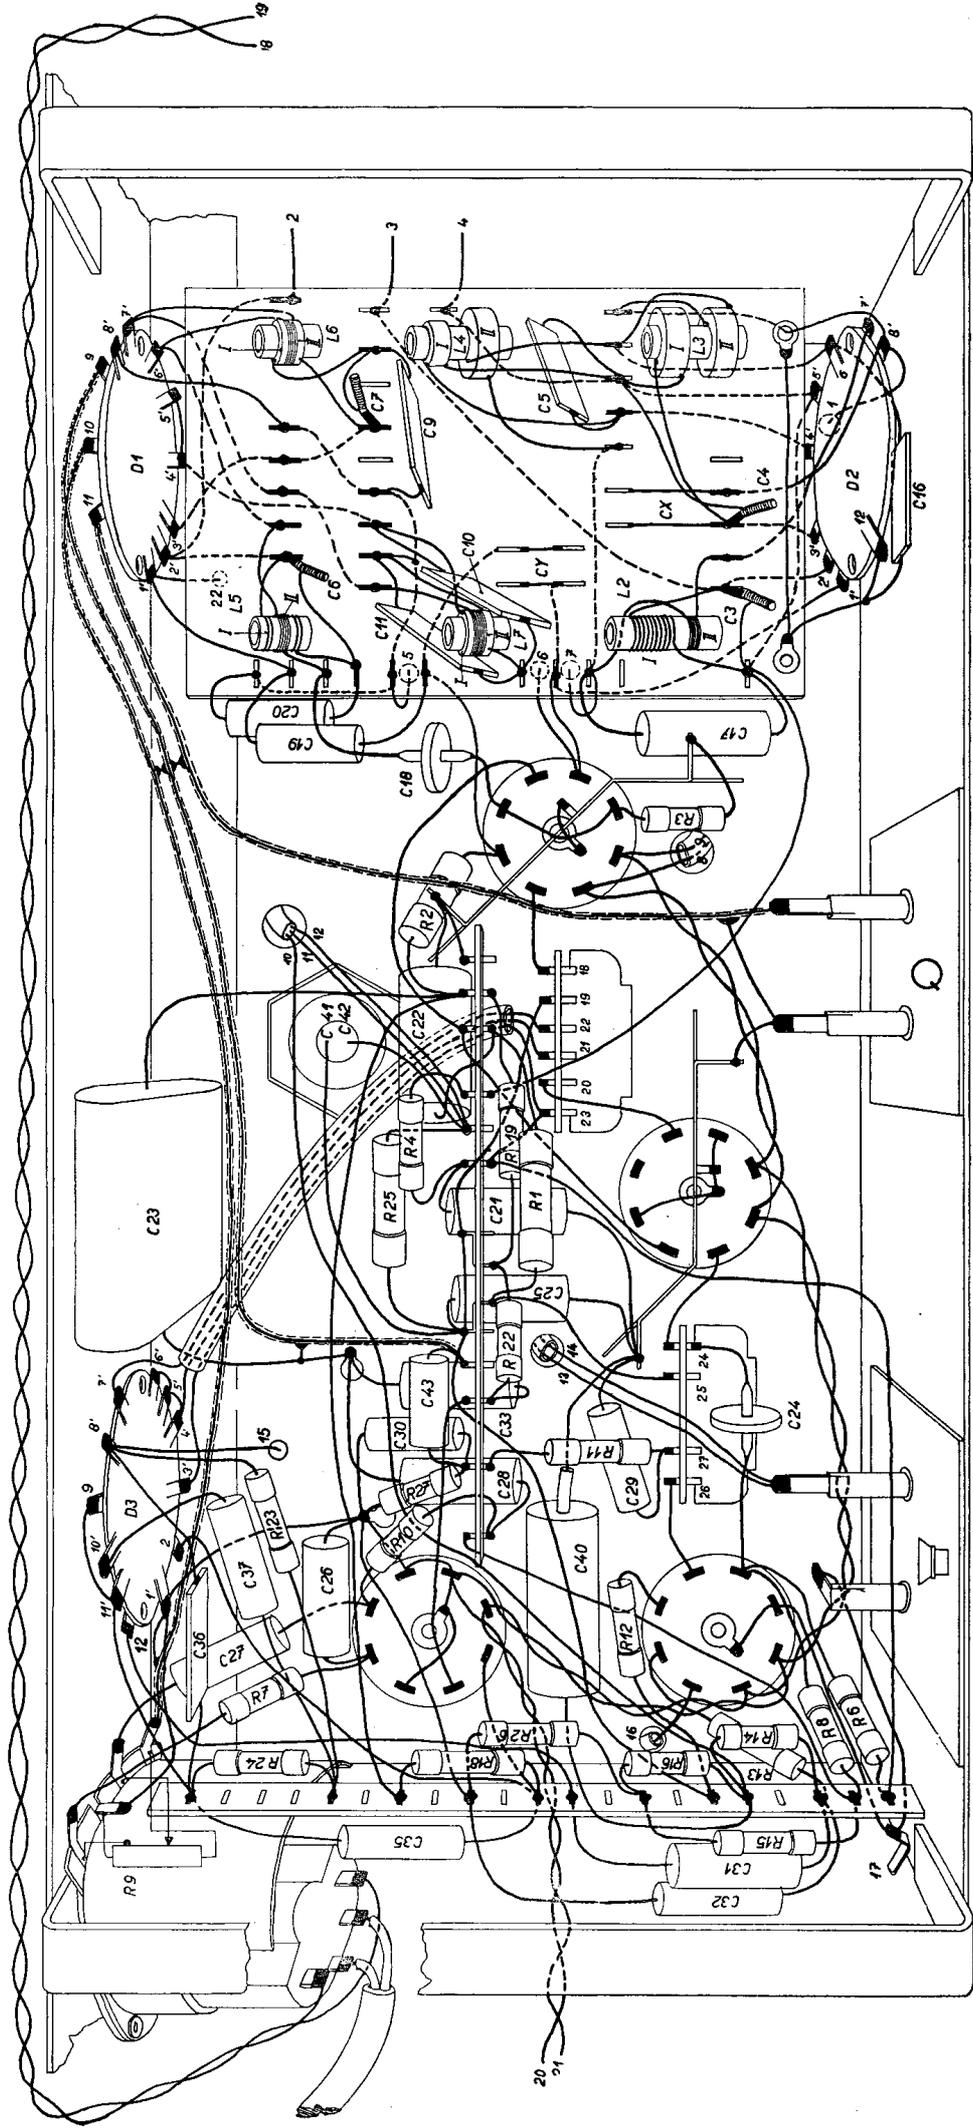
VYVAŽOVACÍ BODY POD CHASSIS
